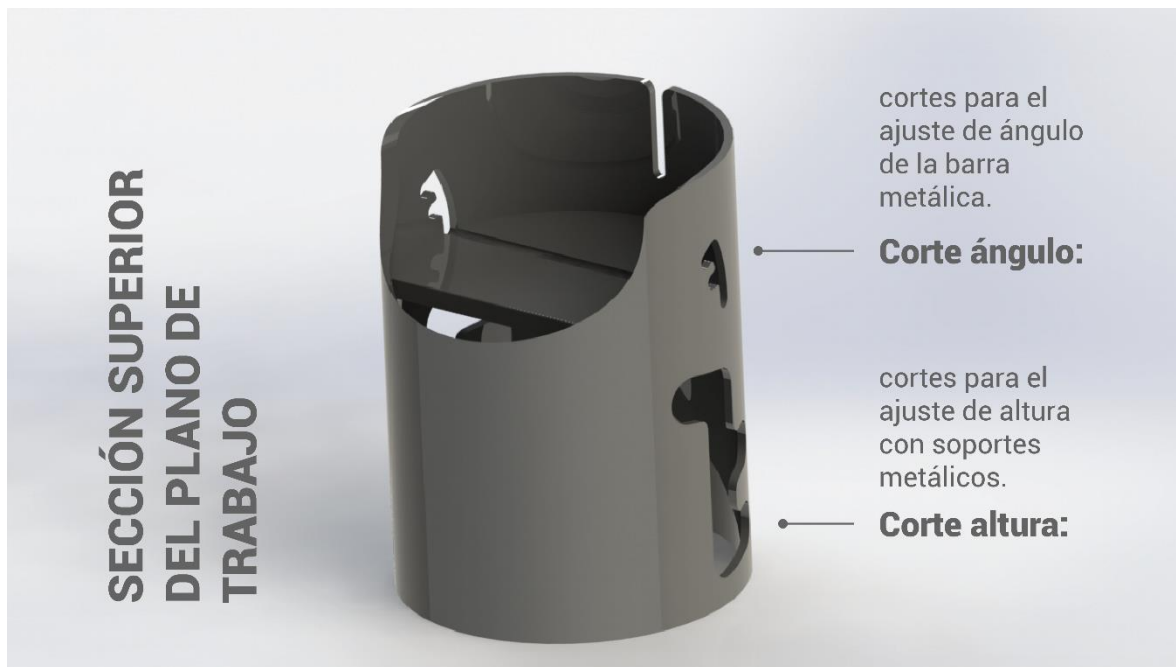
Detalle del diseño: Sección superior del plano de trabajo.
